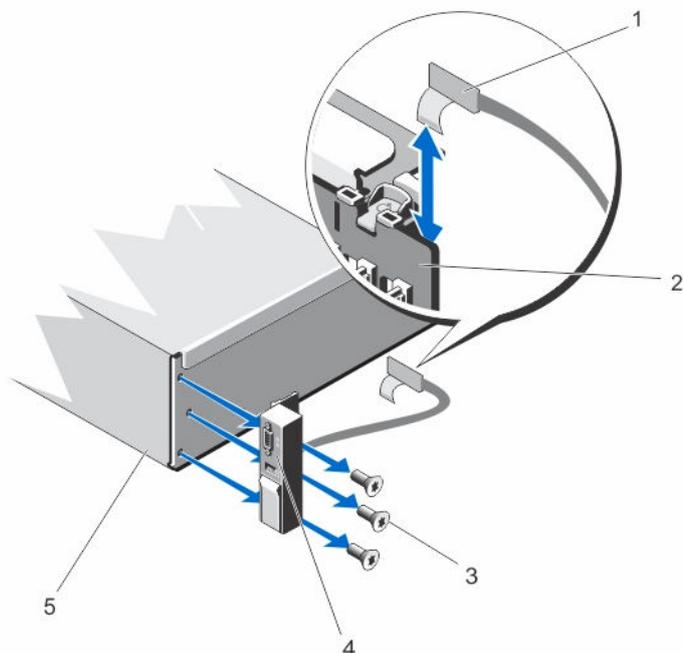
E/A-Platinenbaugruppe entfernen und installieren – PowerEdge R720xd
